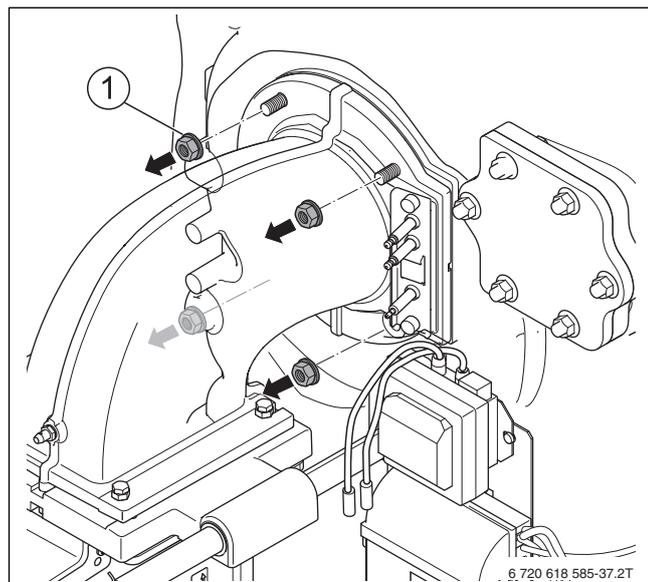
Dévisser les écrous sur le mélangeur coudé
